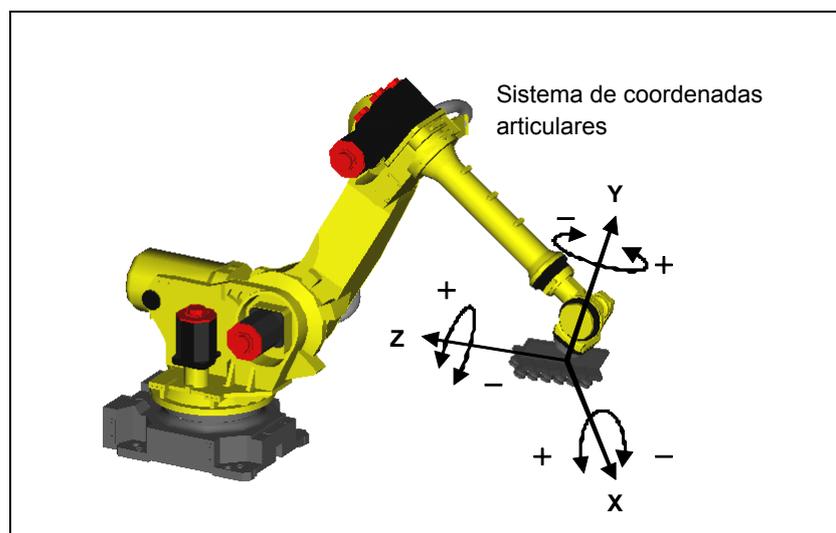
(f) Movimiento de la herramienta (tool)
